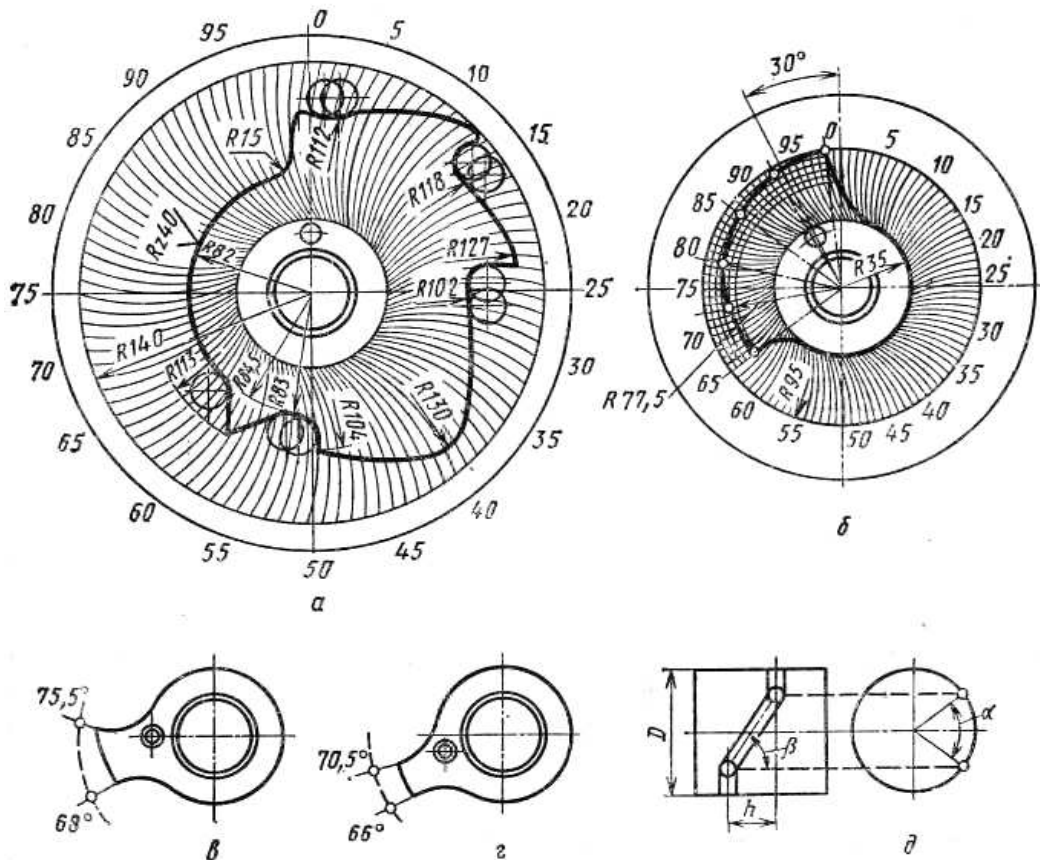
Кулачки токарно-револьверного автомата модели 1E140:
